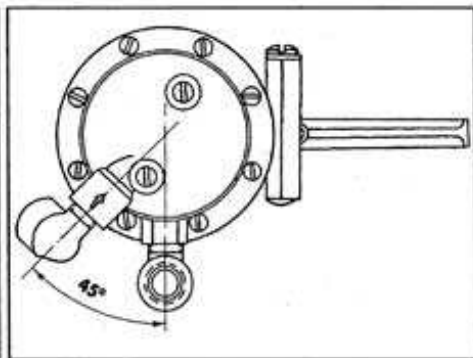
Положение головки и крышки топливного насоса относительно корпуса
